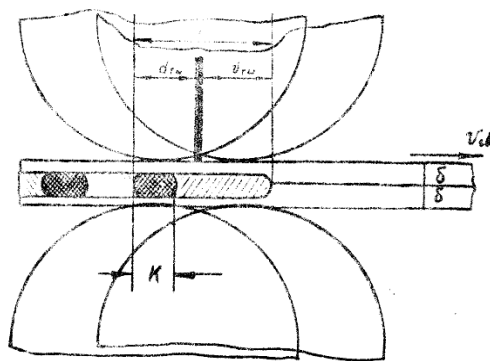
Схема шовной сварки и расчетные размеры сварного соединения
